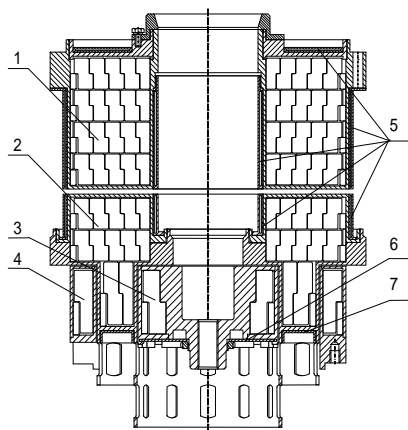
Конструкция АЗ реактора БР-1М: 1 – ВБ; 2 – НБ; 3 – ИБ; 4 – РБ; 5 – борный фильтр; 6 – лист; 7 – кожух
